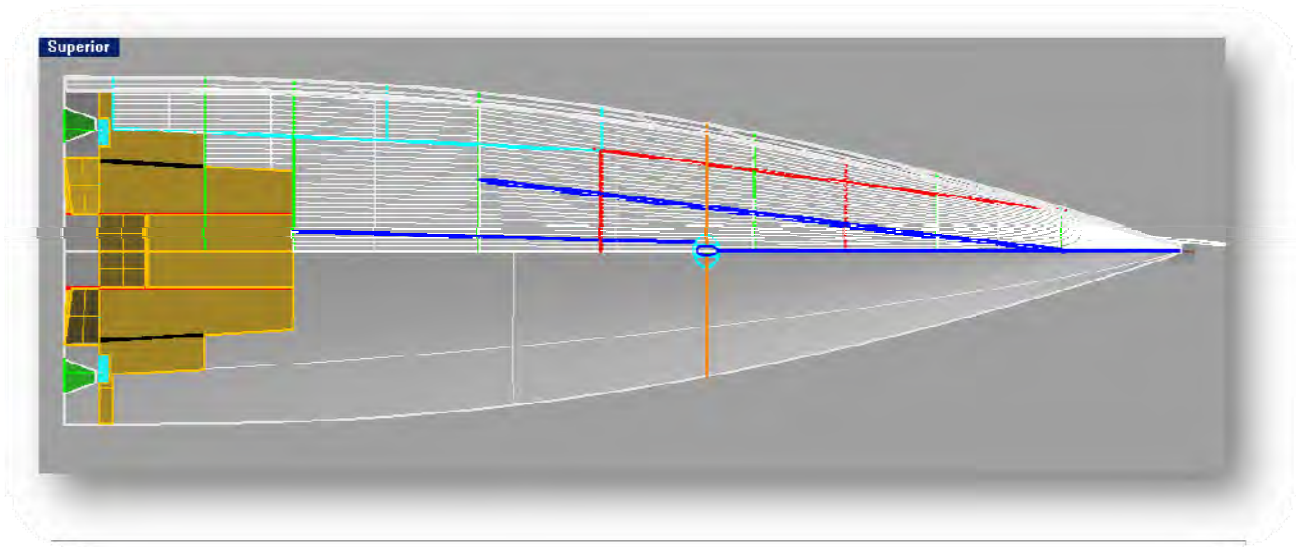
18 Vista en alzado de los refuerzos de la bañera y la cubierta
